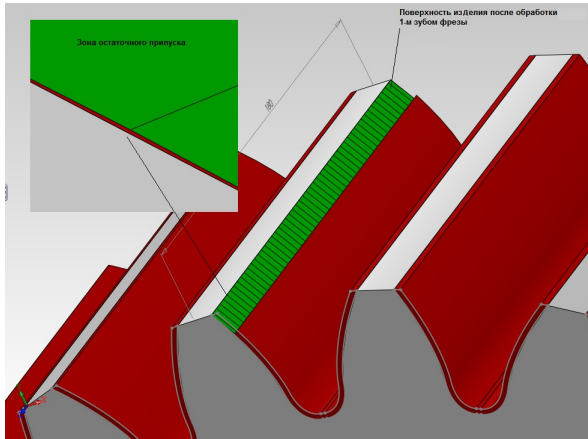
Формоутворення поверхневого шару одним зубом зубооброблючої фрези
